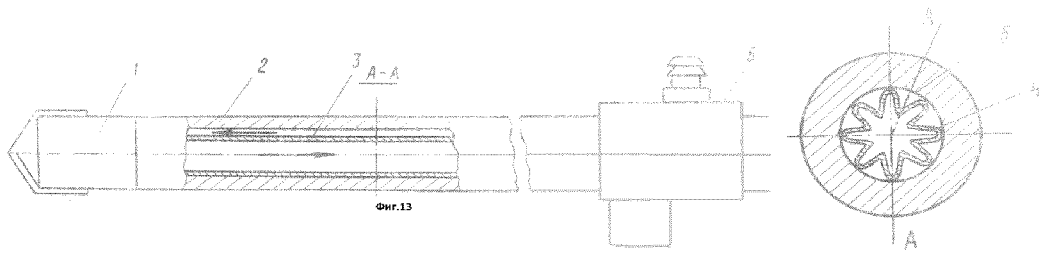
Конструкція ежекторного свердла для гасіння вібрацій
